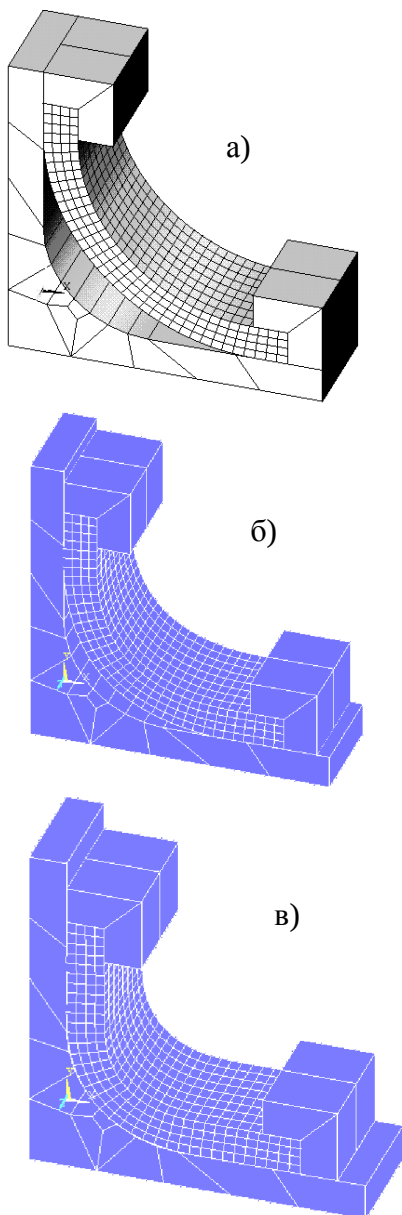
Этапы деформирования заготовки: а – исходное положение; б – положение перед контактом; в – посадка наружного контура заготовки
